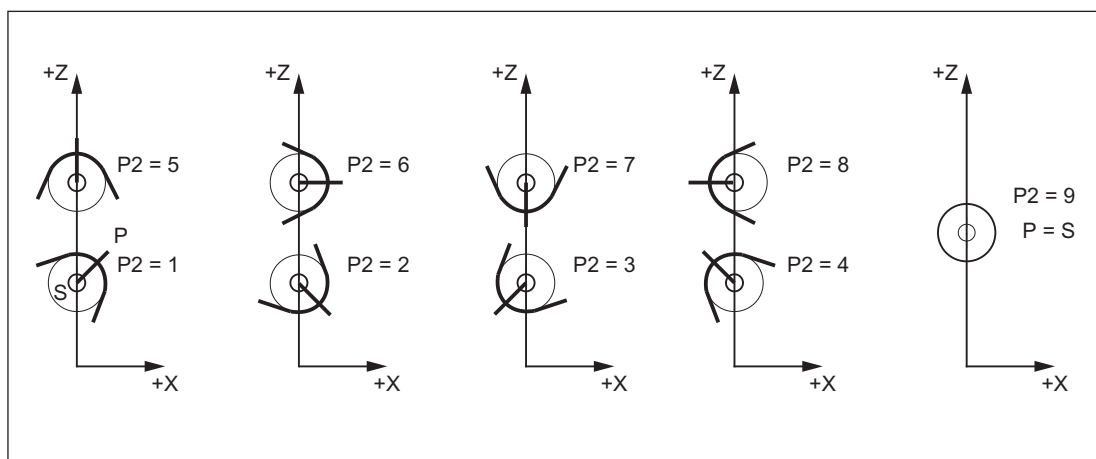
刀具参数 2 (P2)：立式车床上的刀沿位置
